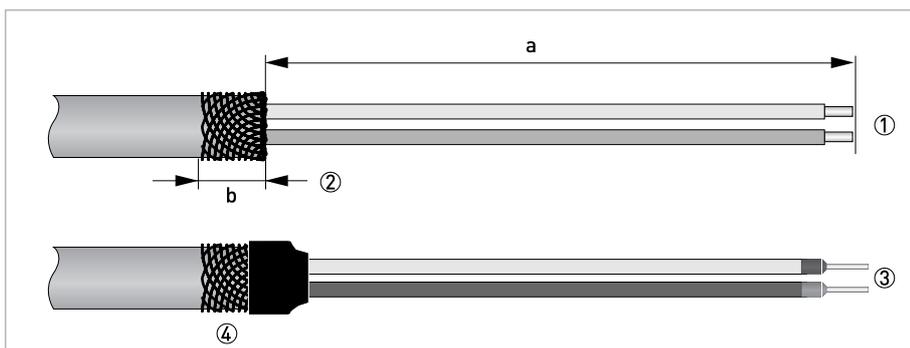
Подготовка кабеля обмотки возбуждения С
